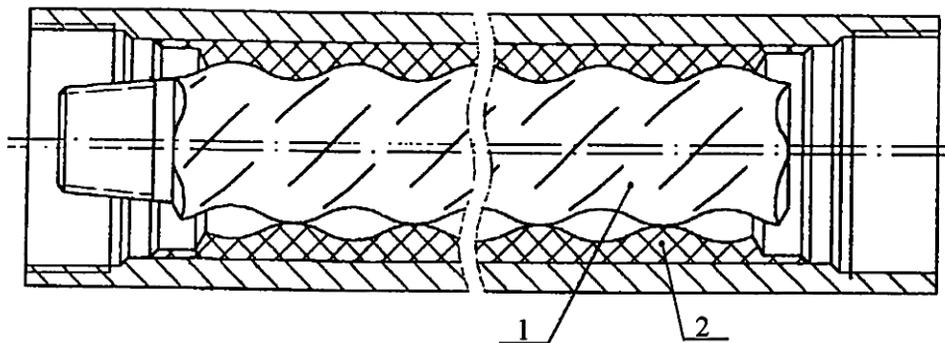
Рабочие органы однозаходного винтового двигателя: 1 – ротор; 2 - статор
